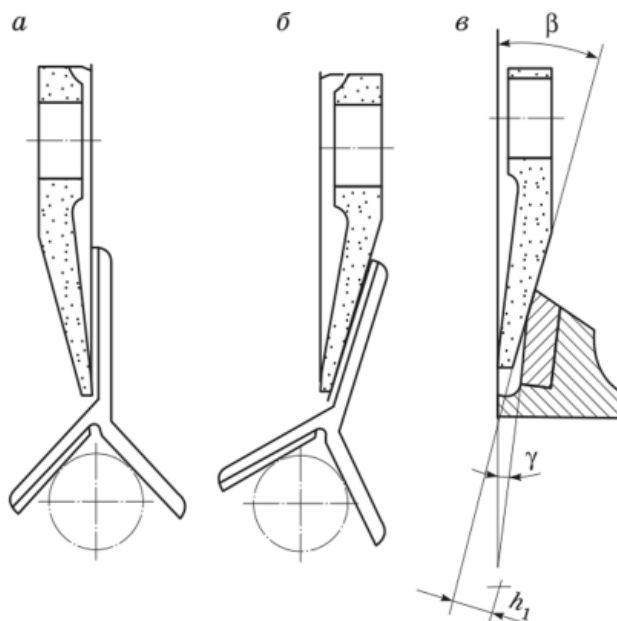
Установка шлифовального круга при заточке передней поверхности развертки
